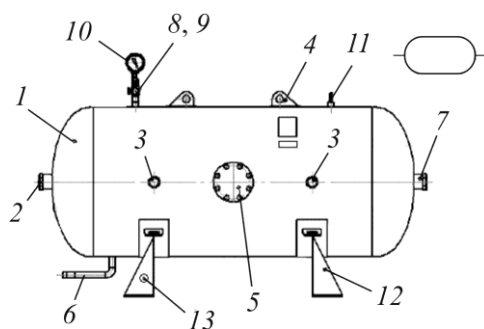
Конструктивная схема ресивера: 1 – сосуд; 2 – вход; 3 – выход; 4 – устройство стоповое; 5 – люк; 6 – слив конденсата; 7 – технологический штуцер; 8 – запорный кран; 9 – ниппель; 10 – манометр; 11 – предохранительный клапан; 12 – опора; 13 – болт заземления
